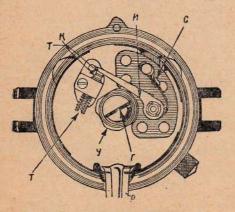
Механический прерыватель. У — кулачковая шайба прерывателя; Г — нажимной винт; Т—неподвижный контакт; К — подвижный контакт; И — рычаг подвижного контакта; С — пружина; Р—рычаг опережения
